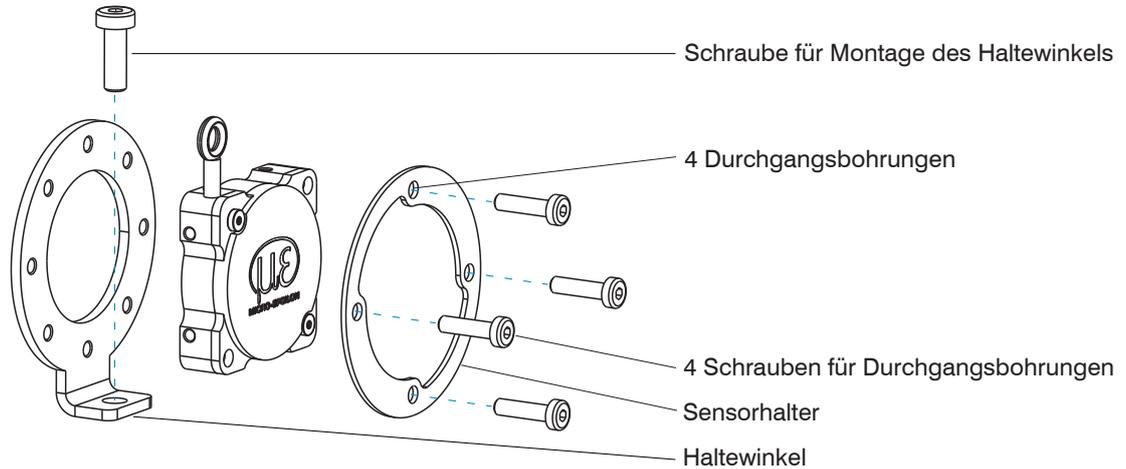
Montage mit Seilaustritt im stufenlosen Winkel (Komplettset), [siehe A 1.2](#)
